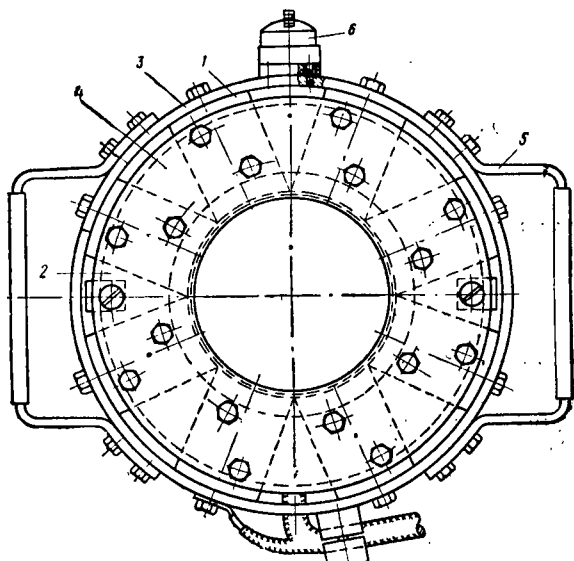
Электрический индукционный нагреватель для съема подшипниковых колец с вала:
